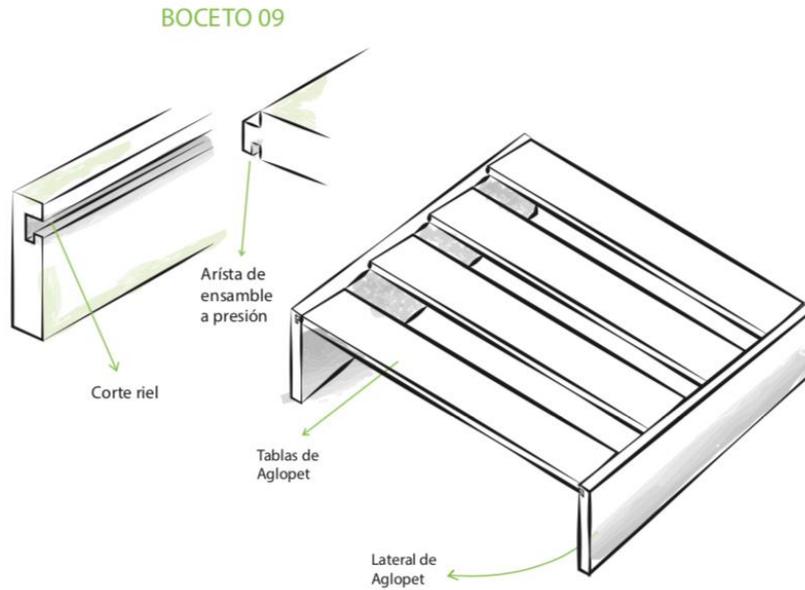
Dibujo técnico alternativa 06. Fuente: La Autora.
